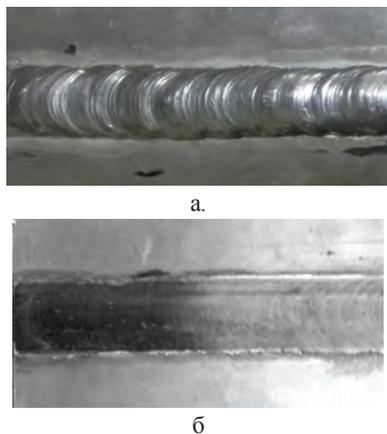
Внешний вид сварного шва до ротационной термопластической обработки (а) и после нее (б)
